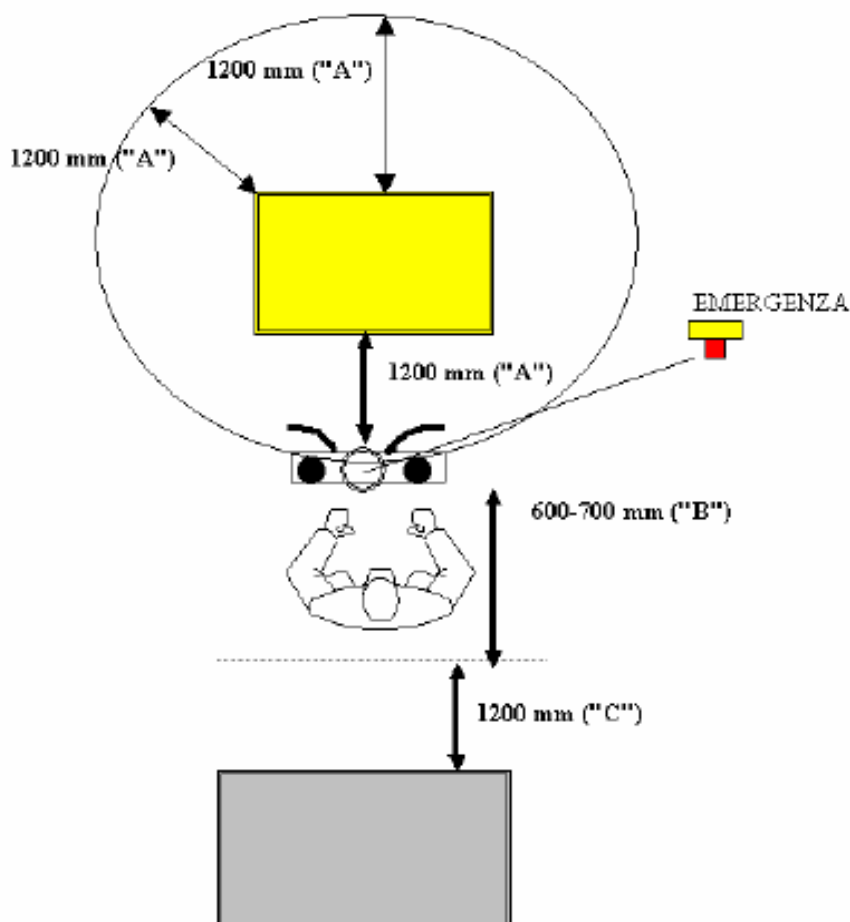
Quote d'installazione della pulsantiera - Vista in pianta
